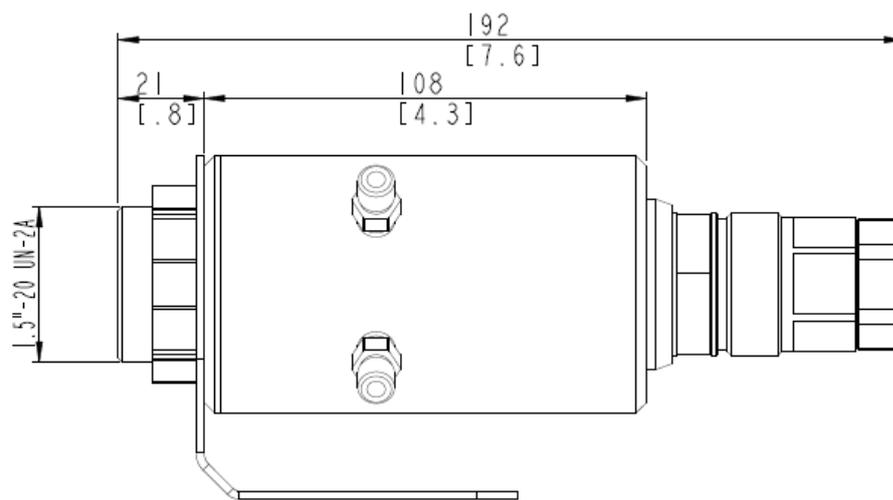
Abmessungen des Sensors mit Schraubklemme und Wasserkühlgehäuse
